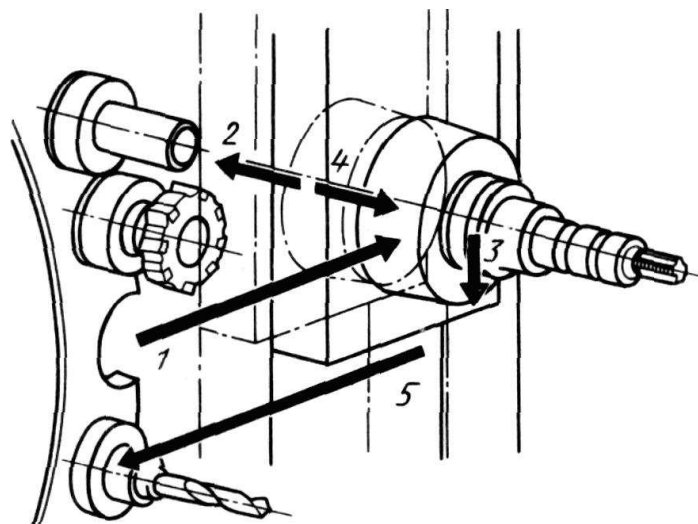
Цикл автоматической смены инструмента в станке с дисковыми инструментальными магазинами
